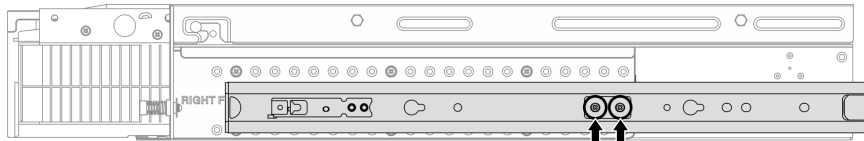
Deux vis pour la glissière interne de Kit de glissières ThinkEdge Friction 1 000 mm v2
